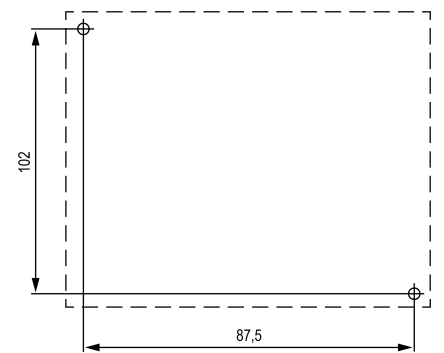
Разметка для монтажа на стену ПР110-х.12х.8х
